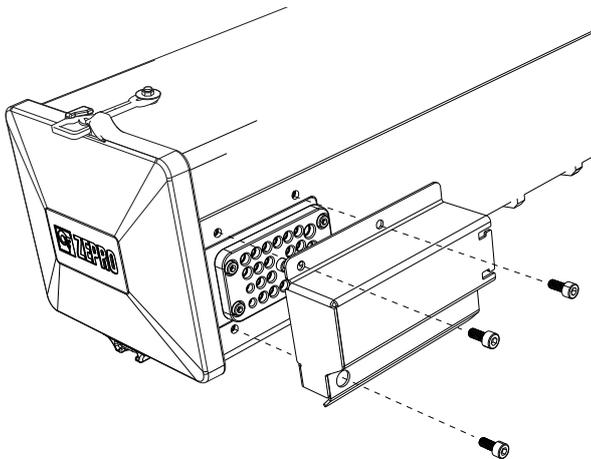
Die Schutzabdeckung der Kabeldurchführung ist mit drei Schrauben befestigt.
